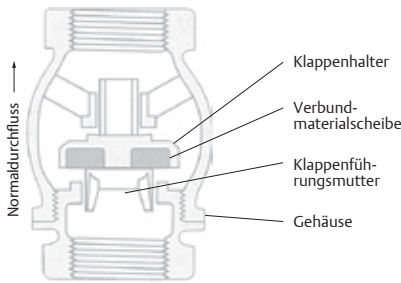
Rückschlagklappe mit vertikalem Hub
